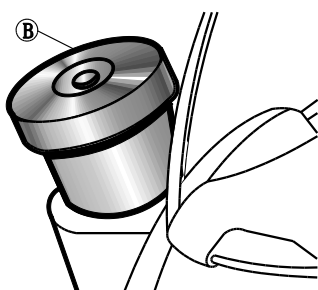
10 Tapa de boquilla de carga de aceite de cámara de engranaje de temporización de motor diesel
